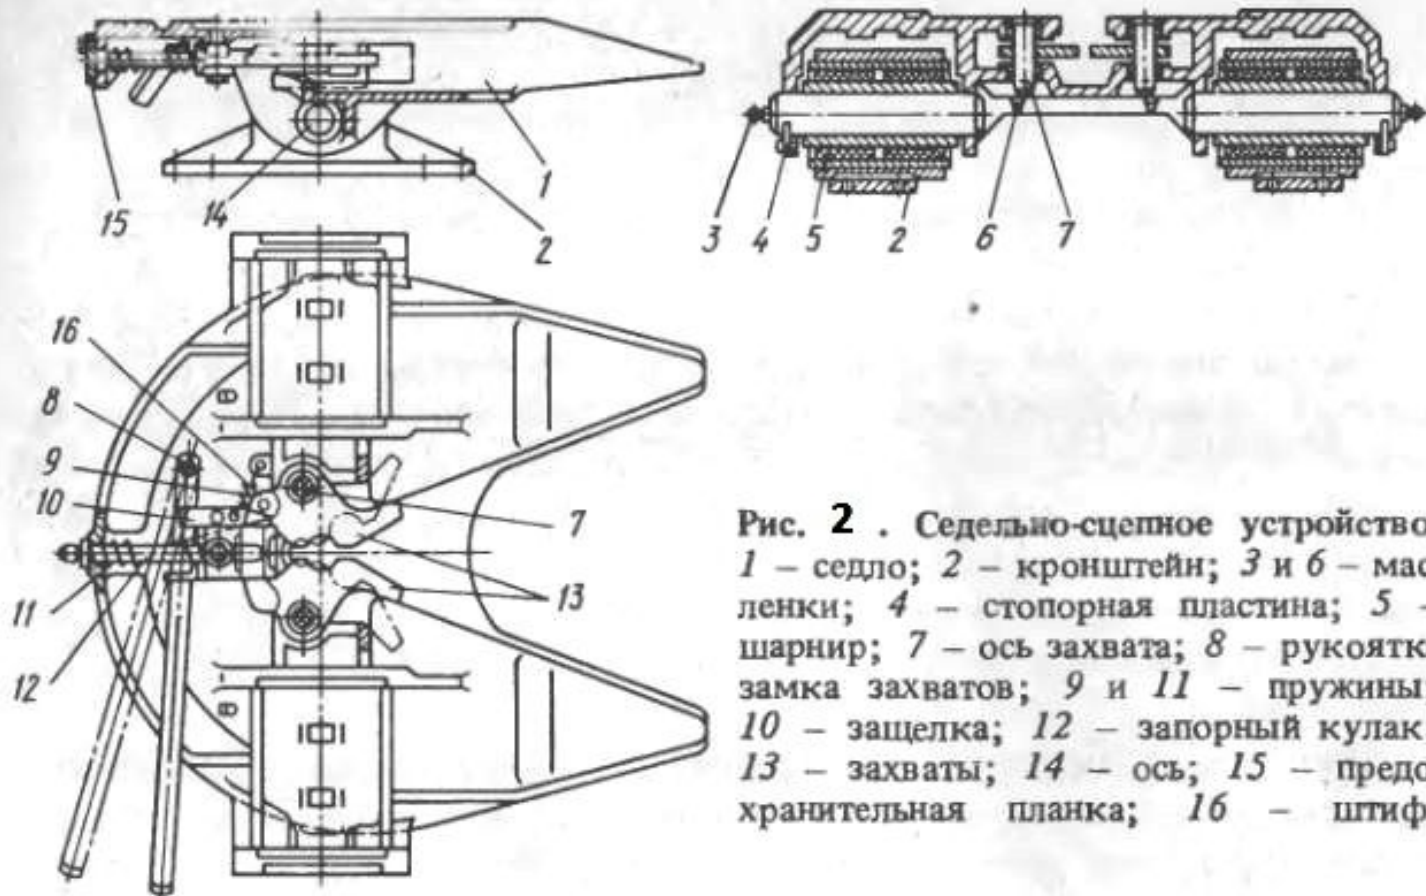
Седельно-сцепное устройство: 1 — седло; 2 — кронштейн; 3 и 6 — масленки; 4 — стопорная пластина; 5 — шарнир; 7 — ось захвата; 8 — рукоятка замка захватов; 9 и 11 — пружины; 10 — защелка; 12 — запорный кулак; 13 — захваты; 14 — ось; 15 — предохранительная планка; 16 — штифт
